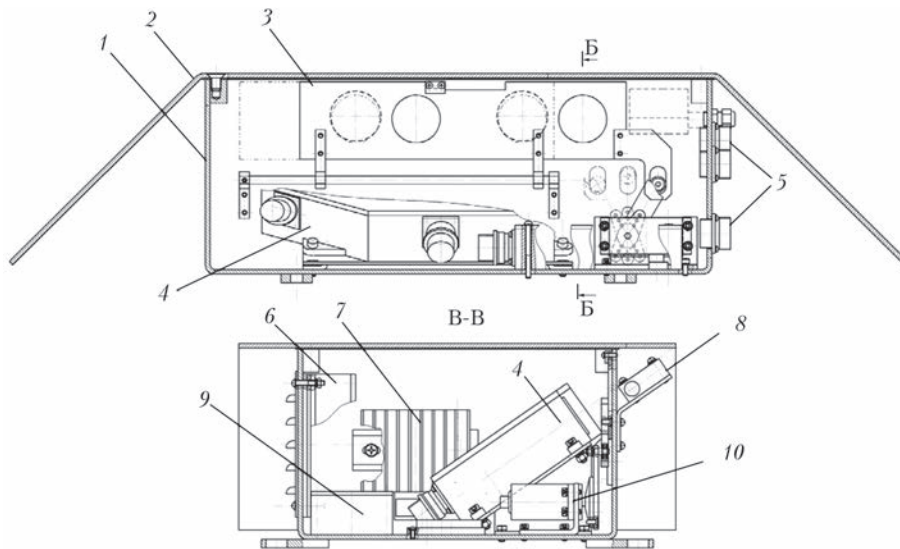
Схема компоновки внутреннего сенсорного блока: 1 – основной корпус; 2 – верхняя защитная панель; 3 – защитная шторка; 4 – лазерно-триангуляционный сенсор; 5 – разъемы; 6 – вентилятор; 7 – нагреватель; 8 – датчик приближения колеса; 9 – блок релейный; 10 – электропривод механизма защитной шторки
